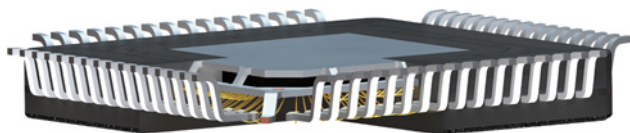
Металлополимерный корпус типа LQFP с теплоотводящей площадкой (exposed pad) и кольцом земли
